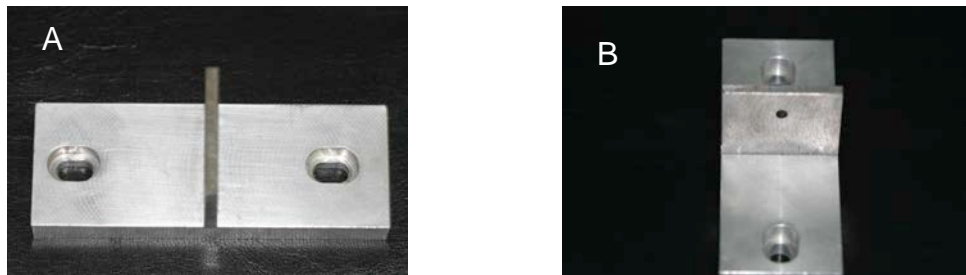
Estrutura metálica para fixação dos CP: a) vista frontal; b) vista lateral
